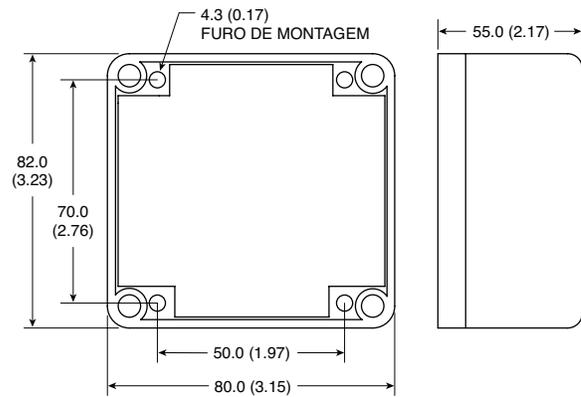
B. Dimensões de montagem UWTC-2-NEMA, UWRTD-2-NEMA
